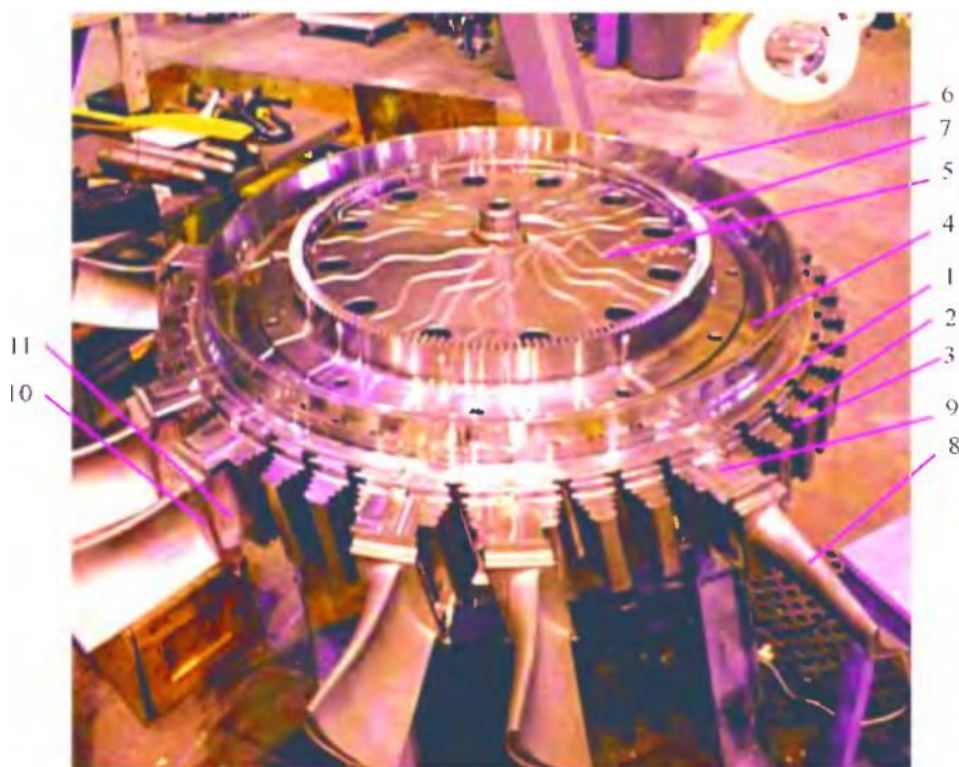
Диск з пазами «ялинкового» типу для установки робочих лопаток: 1 - обід диска; 2 - виступ диска; 3 - паз для лопатки; 4 - полотно; 5 - ступиця; 6 - фланець; 7 - дефлектор; 8 - профільна частина робочої лопатки; 9 - замок; 10 - нижня полиця; 11 – ніжка
